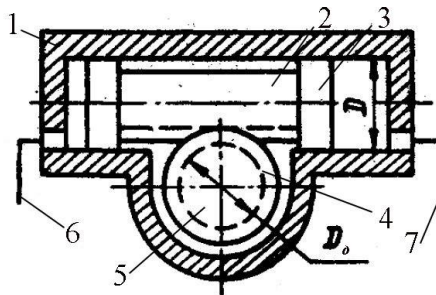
Поршковий поворотний гідродвигун: 1 – корпус; 2 – шток із рейково-зубчастою передачею; 3 – поршні; 4 – шестерня; 5 – вал рейкової шестерні; 6, 7 – канали
